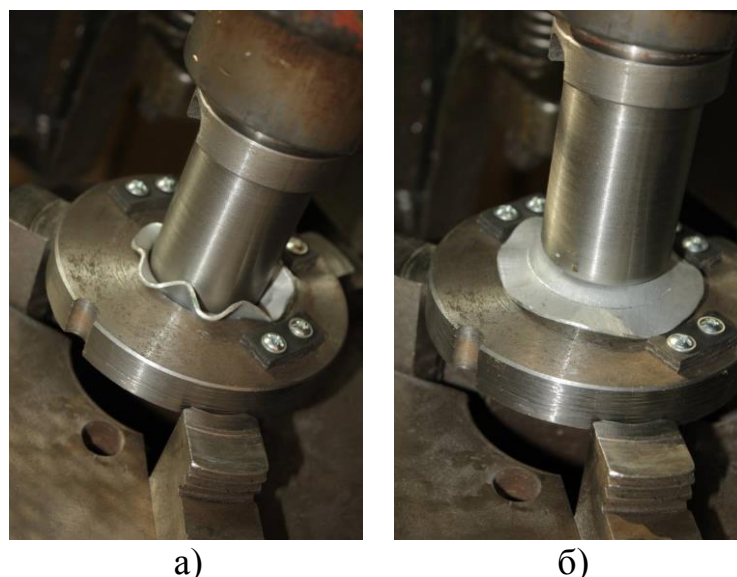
Витягування з кантуванням заготовки (матеріал – алюміній А2; діаметр заготовки – $D_{заг} = 86$ мм): а – прямий хід пуансона (4-е кантування заготовки); б – зворотній хід пуансона (5-е кантування заготовки)
